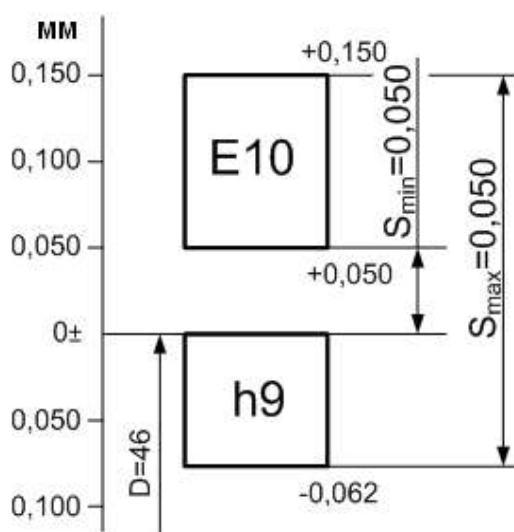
Схема розташування полів допусків деталей з'єднання Ø46E10/h9
